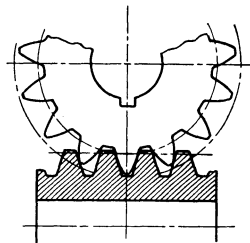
Schneckenrad mit korrigierter Zahnform.
